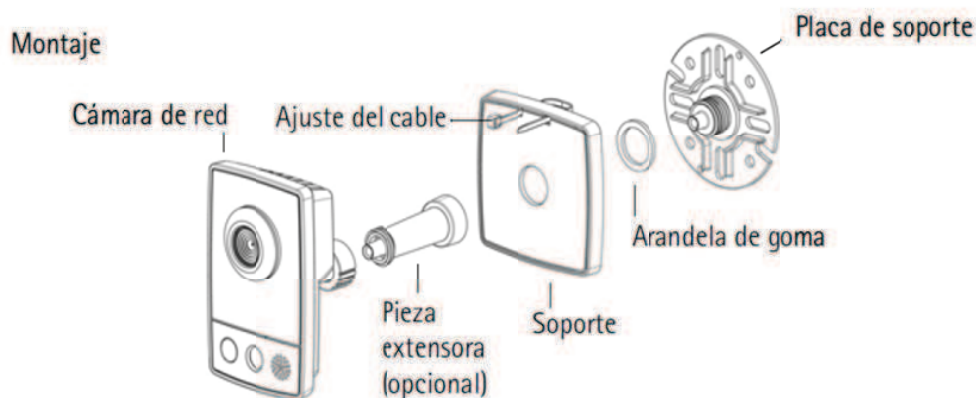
Montaje de la cámara IP Axis M1031-W ^[62]
